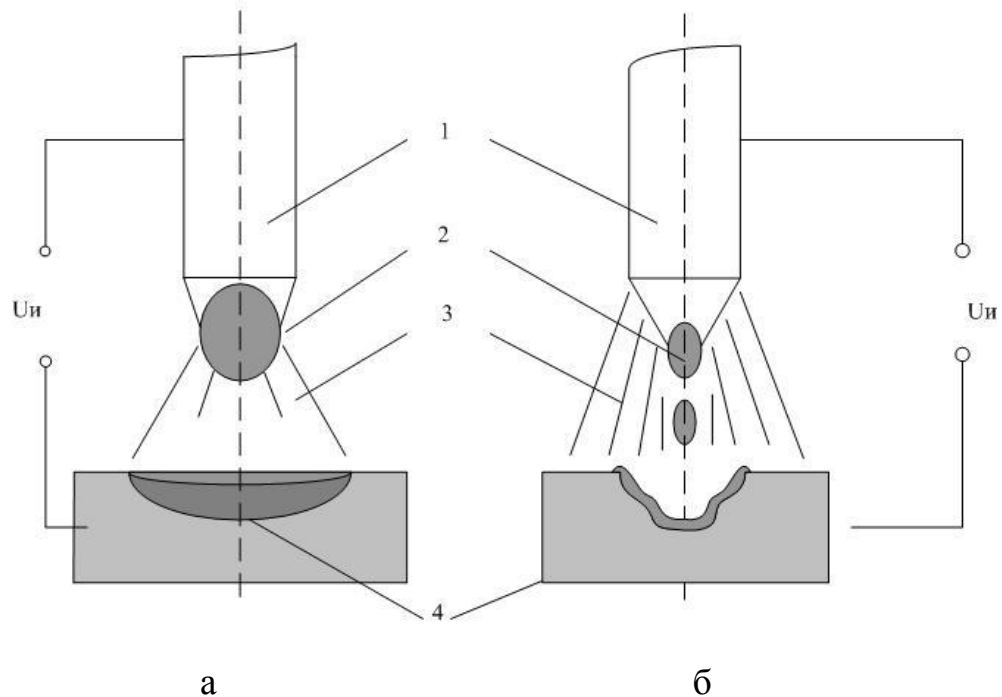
Разновидности переноса металла в дуге: а) крупнокапельный, б) мелкокапельный, 1- сварочная проволока; 2 - капля расплавленного металла; 3 - сварочная дуга; 4 - сварочная ванна.
